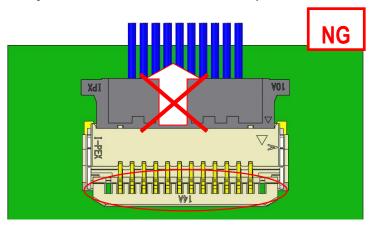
PLUG の抜去方法 (NG) / Fig.18 To withdraw PLUG (NG)
